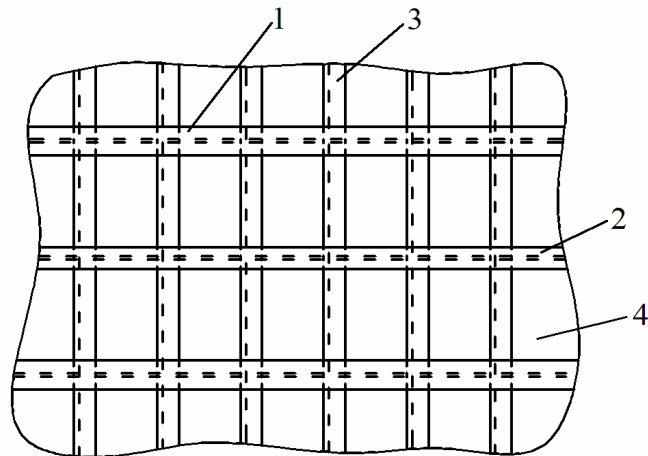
Схема установки дополнительного бортового стрингера перекрытия (1 – основной бортовой стрингер; 2 – дополнительный бортовой стрингер; 3 – штатный шпангоут; 4 – обшивка борта)
